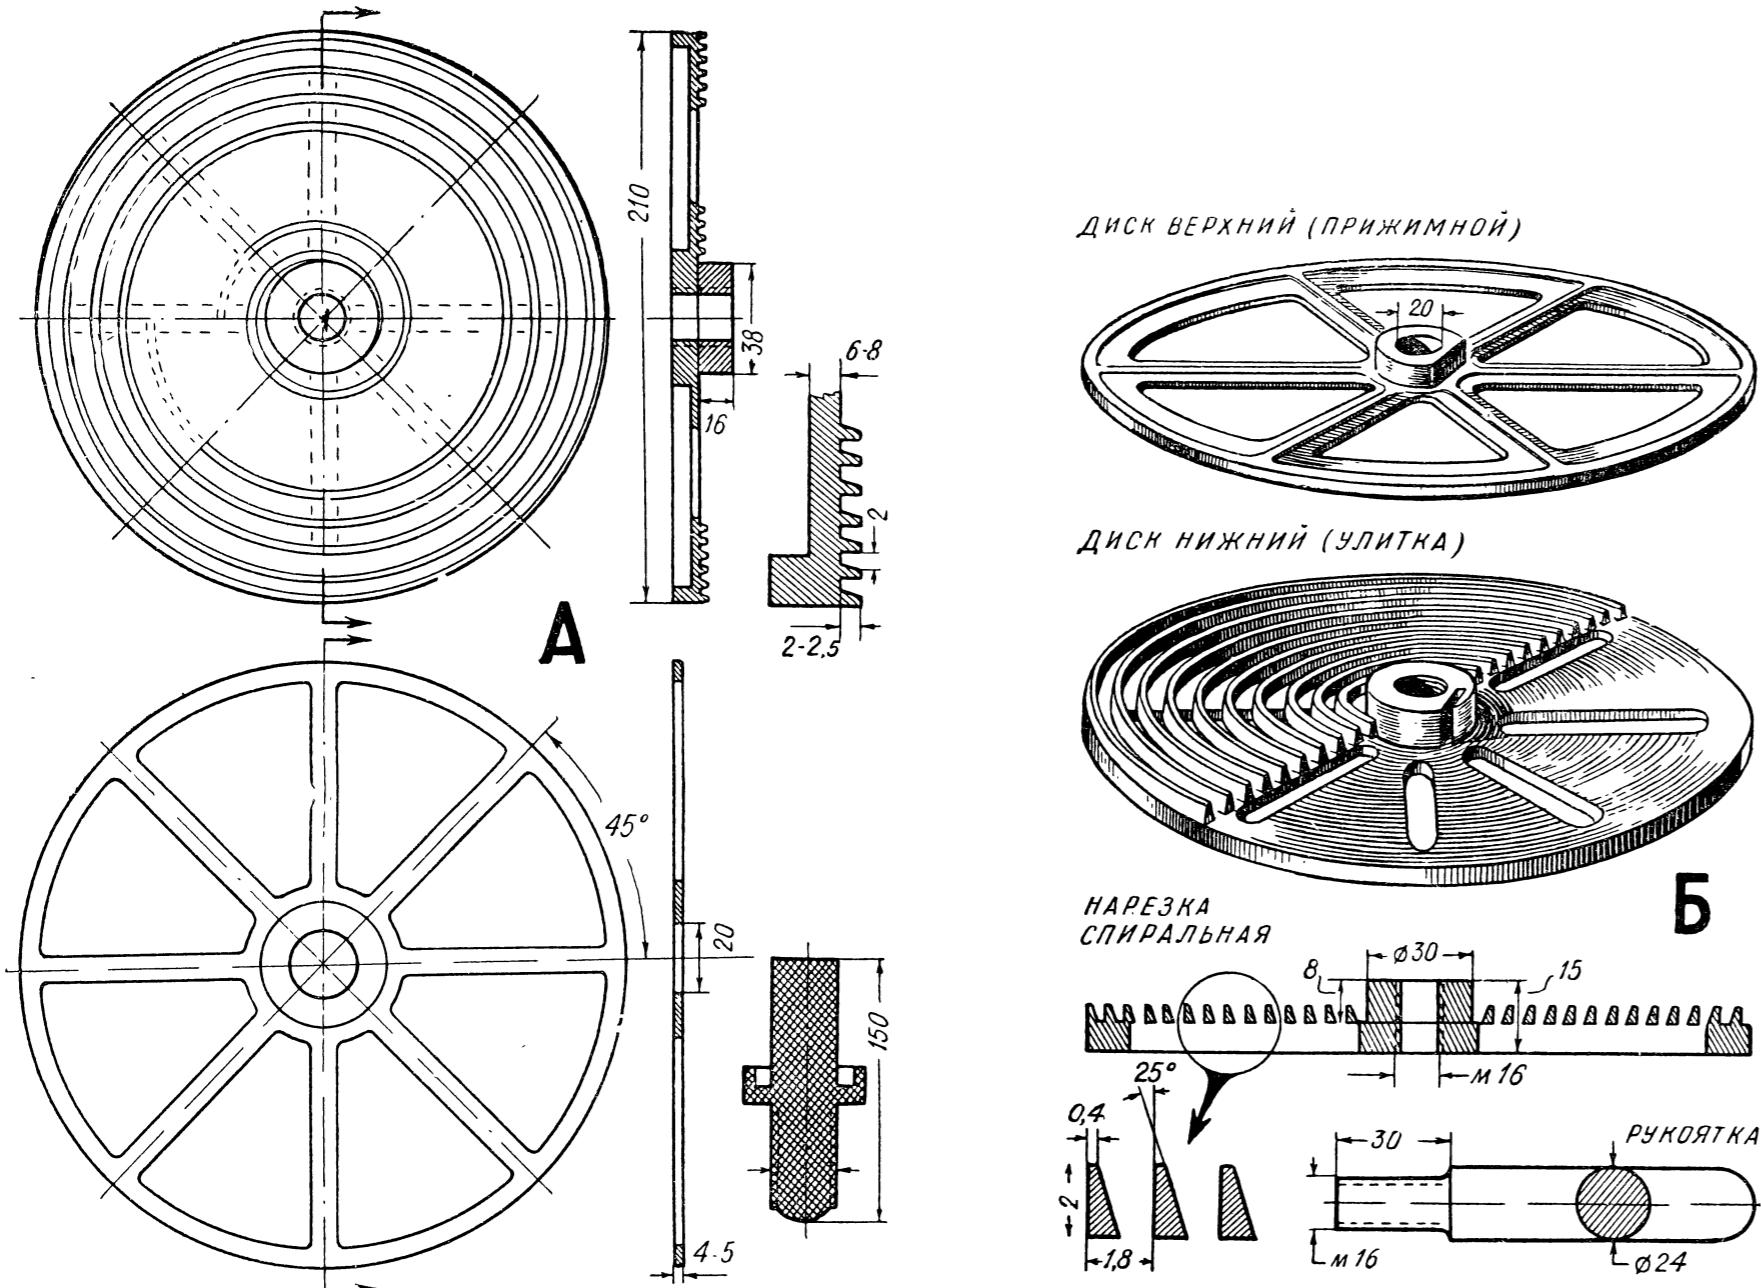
Спиральный проявочный прибор: А — для 16 мм ленты; Б — для 8 мм ленты
